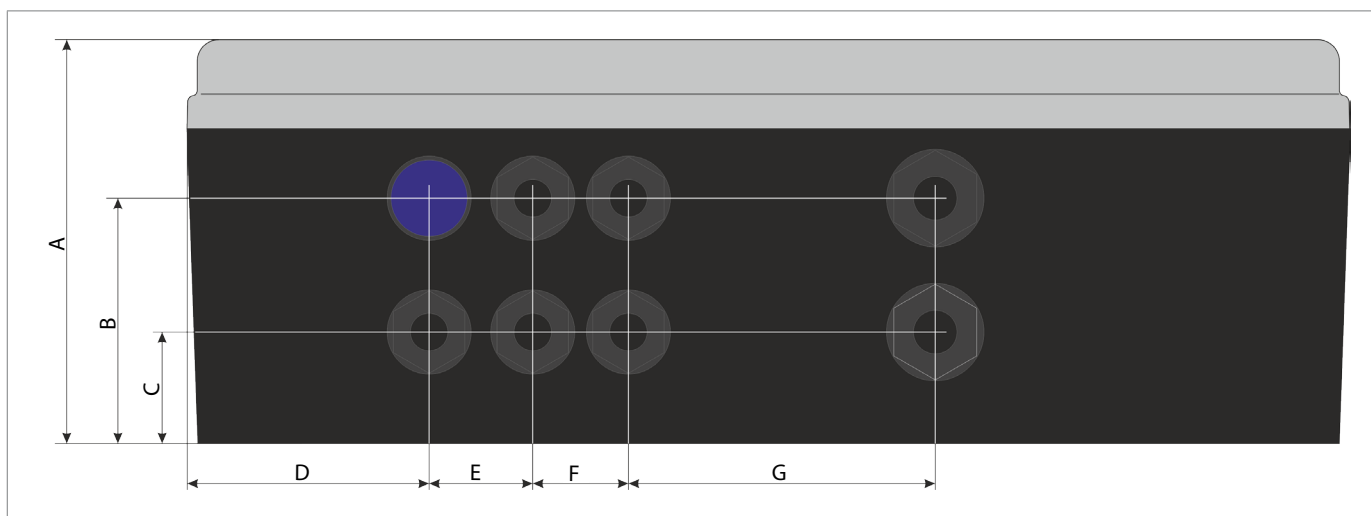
Vista esterna lato inferiore versione pressacavi
